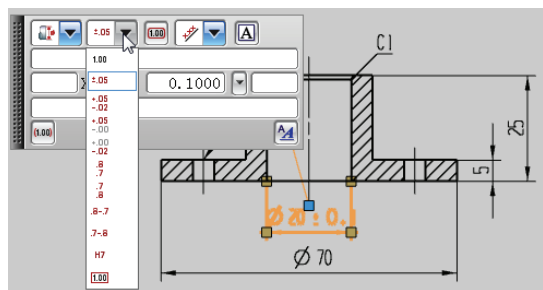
利用屏显编辑栏为尺寸添加尺寸公差
